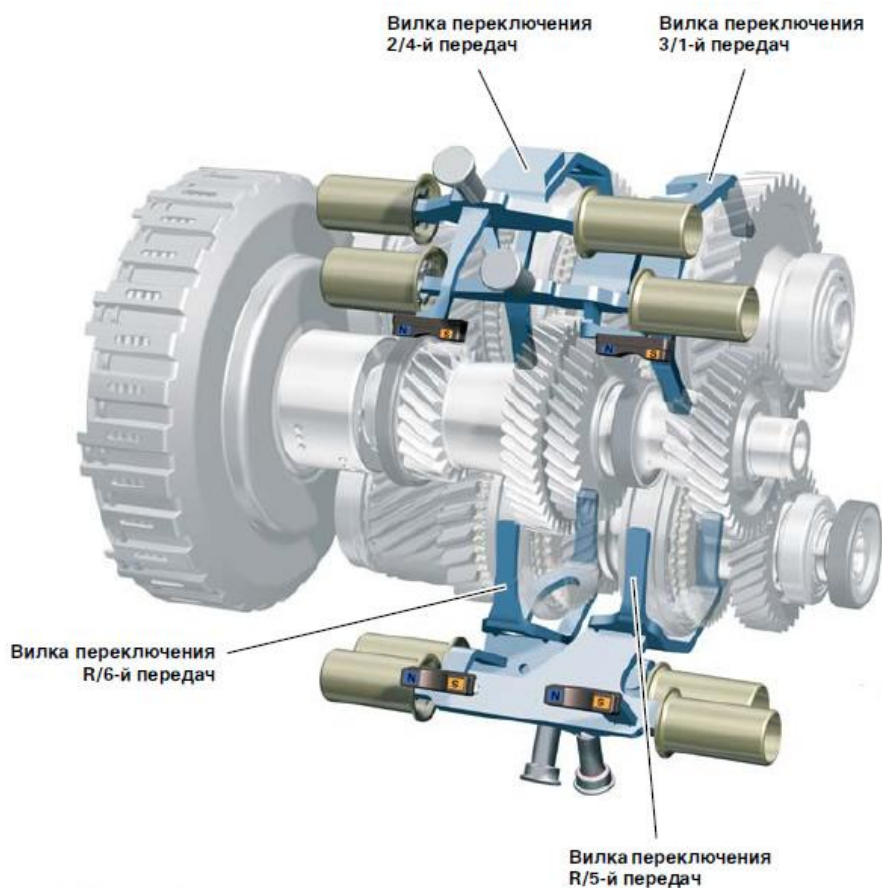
Переключение блоков зубчатых колес с помощью вилок и гидроцилиндра
